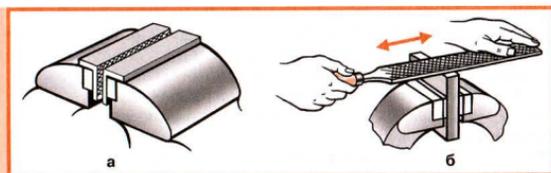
Нагубники (а) и зачистка заготовки напильником (б)
